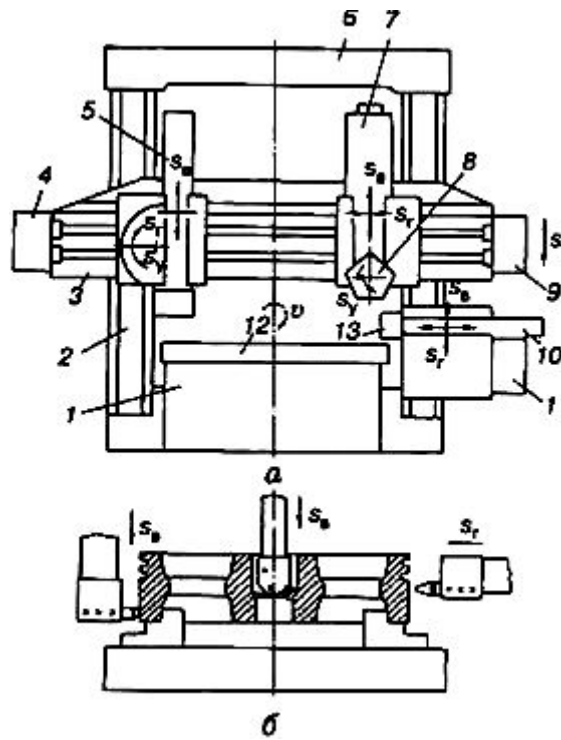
Загальний вигляд токарно-карусельного верстата і обробка деталі на ньому
